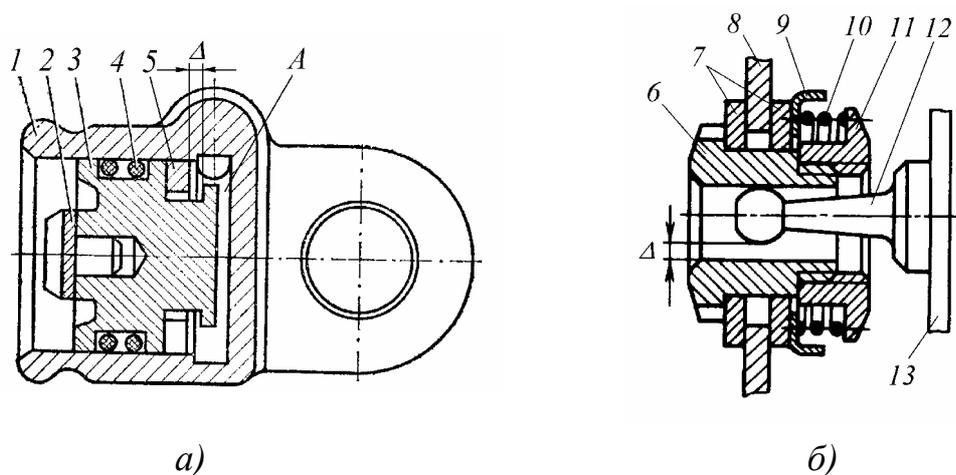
Устройства автоматической регулировки зазора между фрикционной накладкой и тормозным барабаном:
